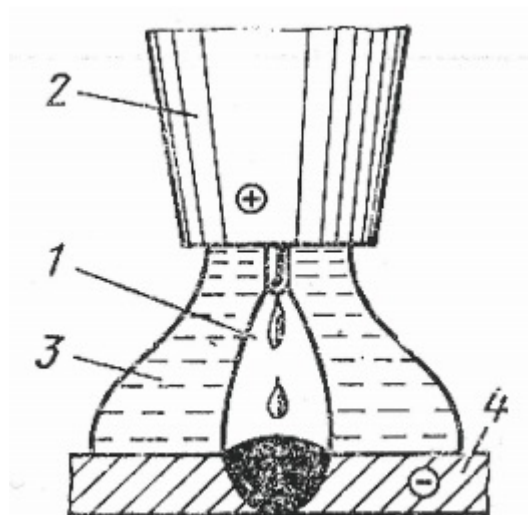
Дуговая сварка в защитных газах
